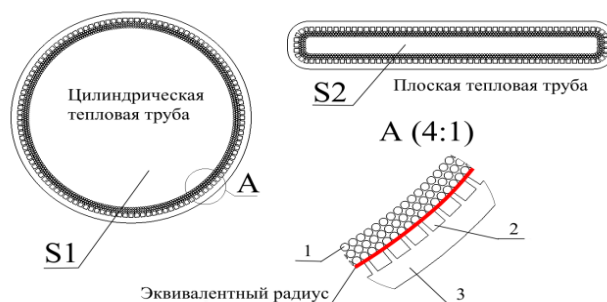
Внутренне строение цилиндрической ТТ с составным фитилем: 1 – пористый фитиль, 2 – канавчатый фитиль, 3 – металлический корпус; S1 – площадь газового канала цилиндрической ТТ; S2 – площадь газового канала плоской ТТ
